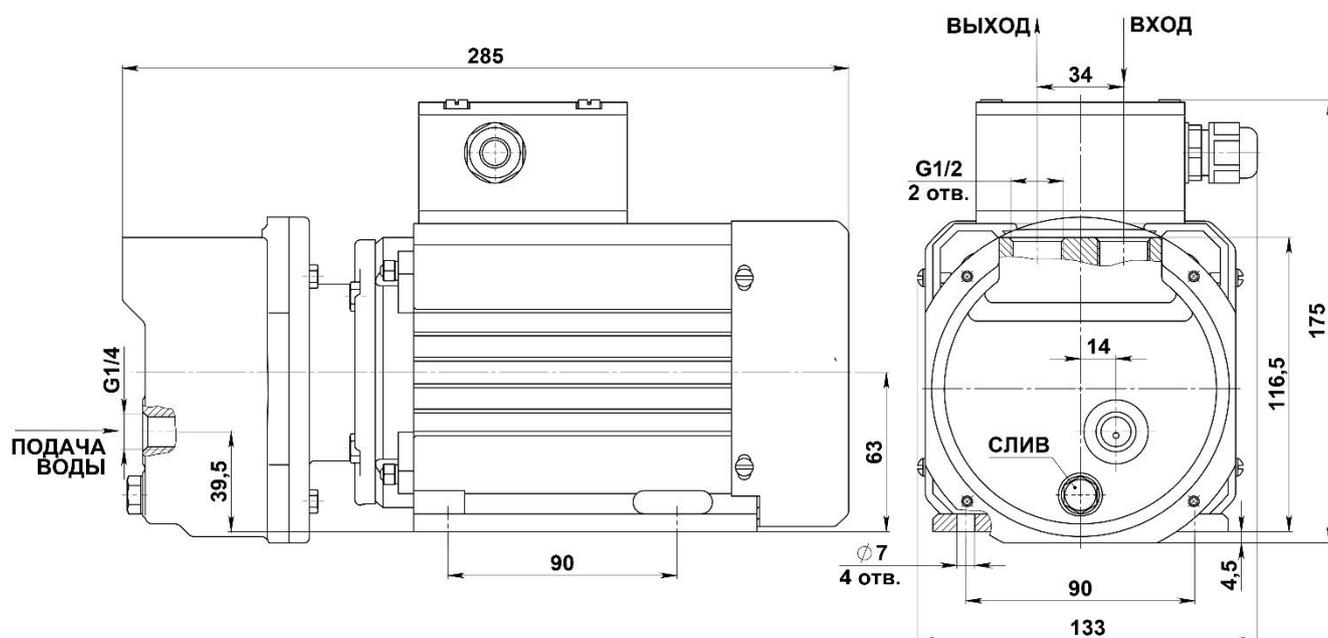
Габаритные и присоединительные размеры насоса HBV-12.
